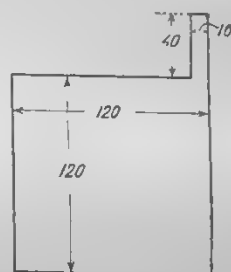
Размеры и форма пластин (из ролного свинца) для изготовления аккумулятора накала.
